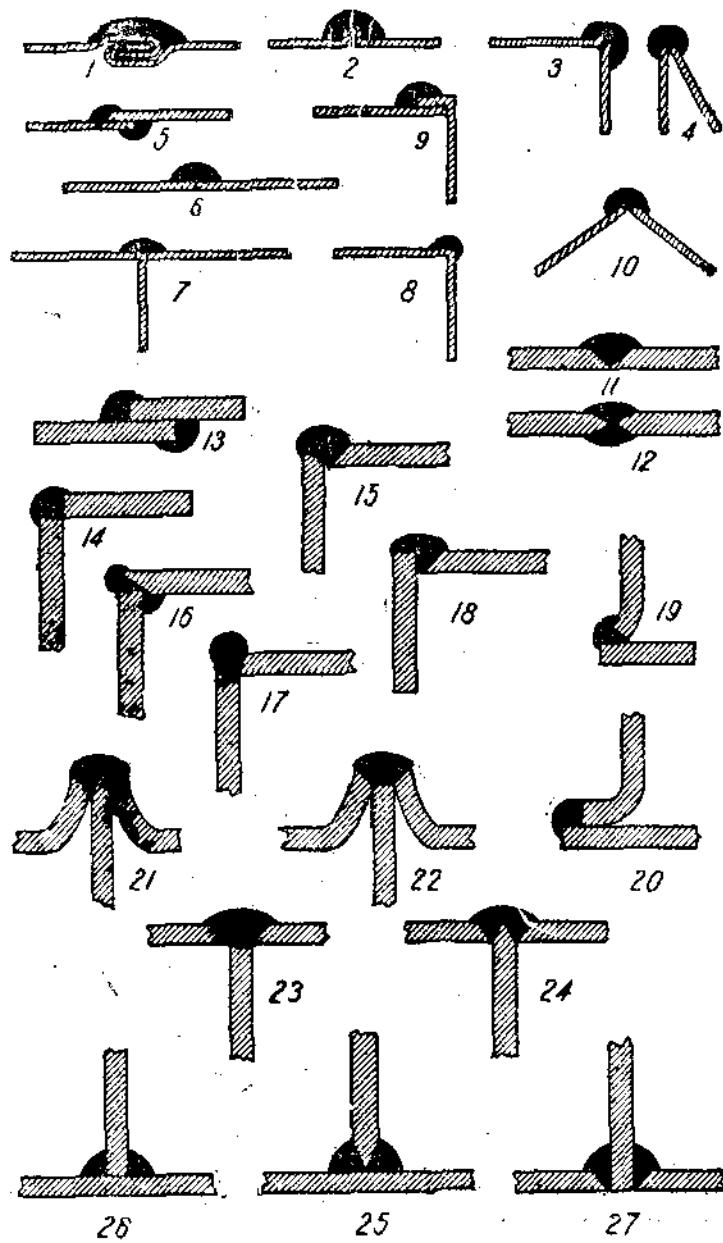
и 12. Самые простые способы сварки сстык: V-образный и X-образный.
